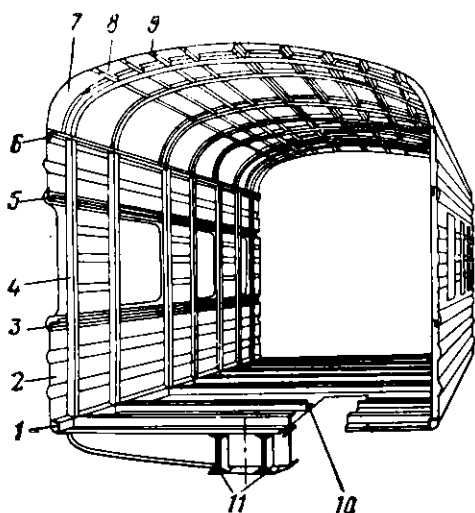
Каркас кузова цельнометаллического вагона с хребтовой балкой
